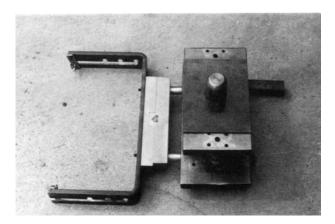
Нижнее центровочное приспособление в зацеплении
